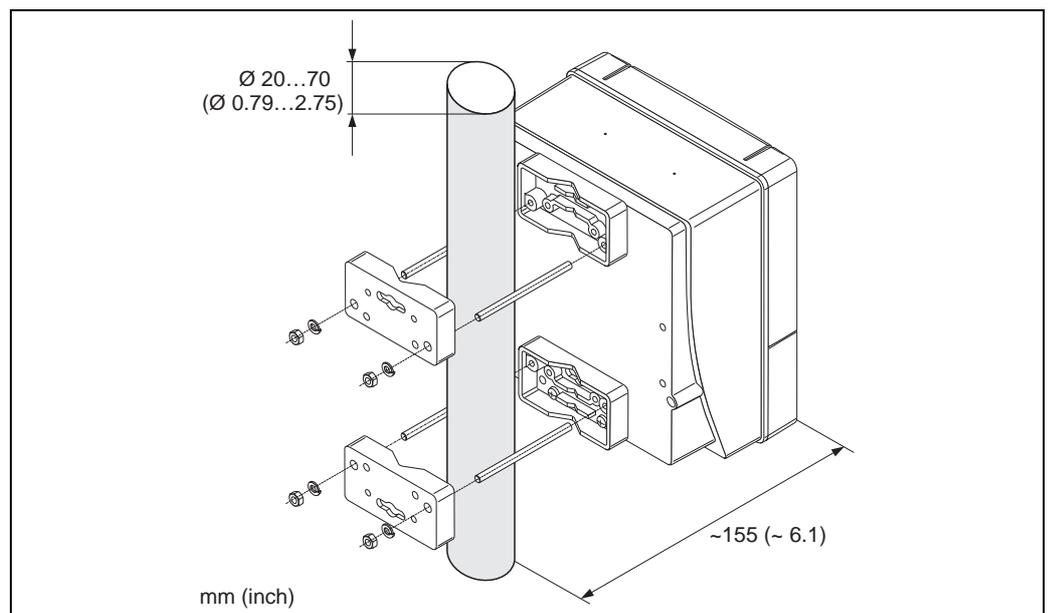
Rohrmontage (Wandaufbaugeschäuse)
